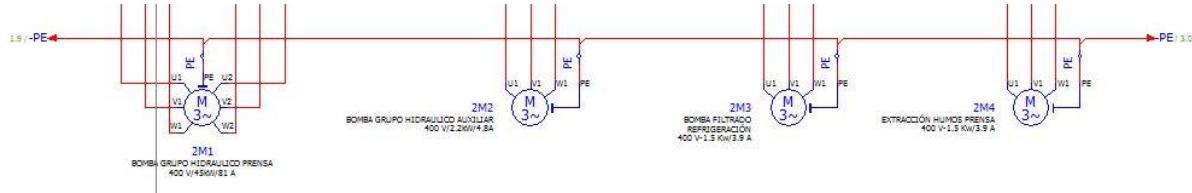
Motores de la moldeadora (extracto de los anexos)
